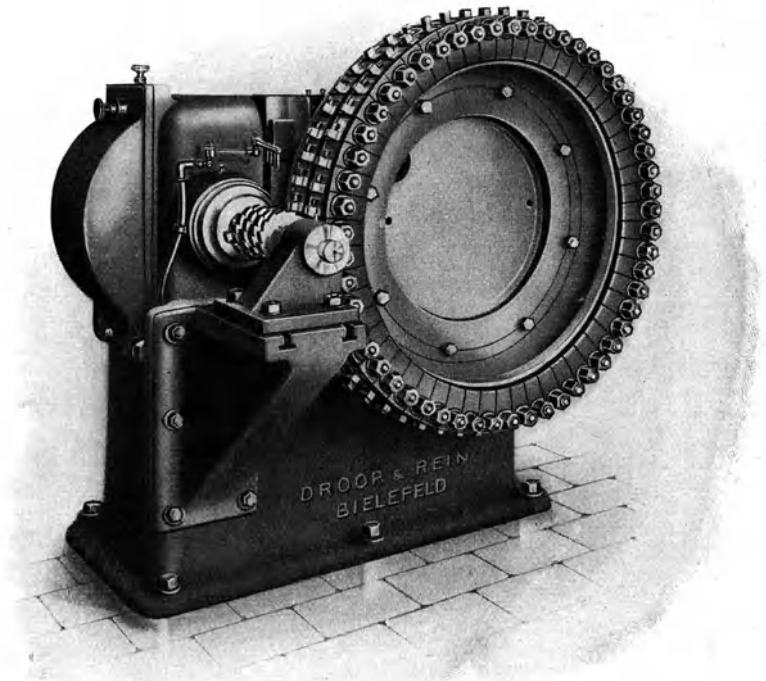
Sonderfräsmaschine von Droop u. Rein, Bielefeld.
